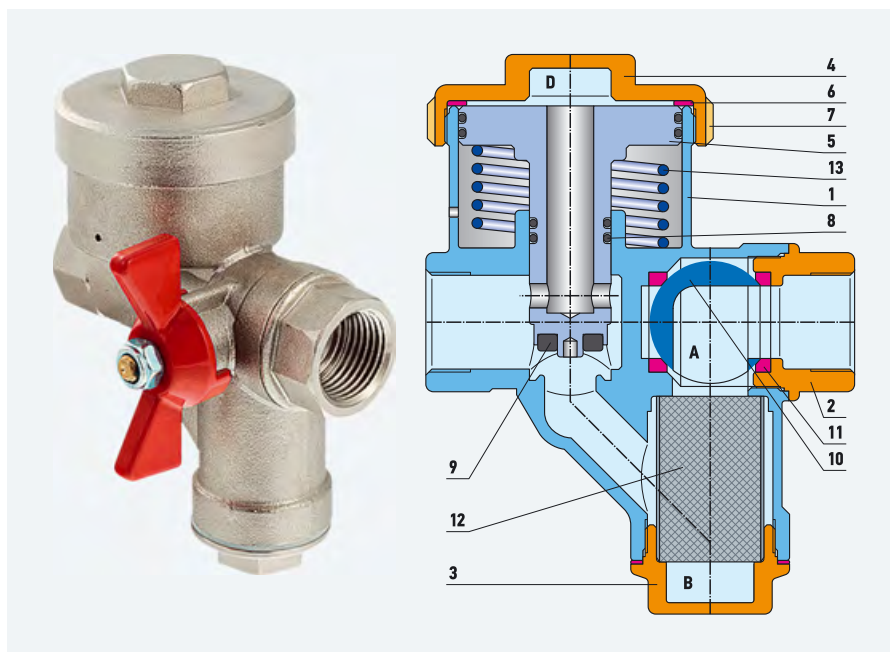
Поршневой редуктор VT.087 (1 — корпус; 2 — крышка корпуса; 3 — пробка; 4 — поршень; 5 — золотник; 6 — гайка; 7 — упорный конус; 8 — гайка настройки; 9 — защитный колпачок; 10 — пружина; 11 — большое уплотнительное кольцо; 12 — малое уплотнительное кольцо; 13 — прокладка золотника)
